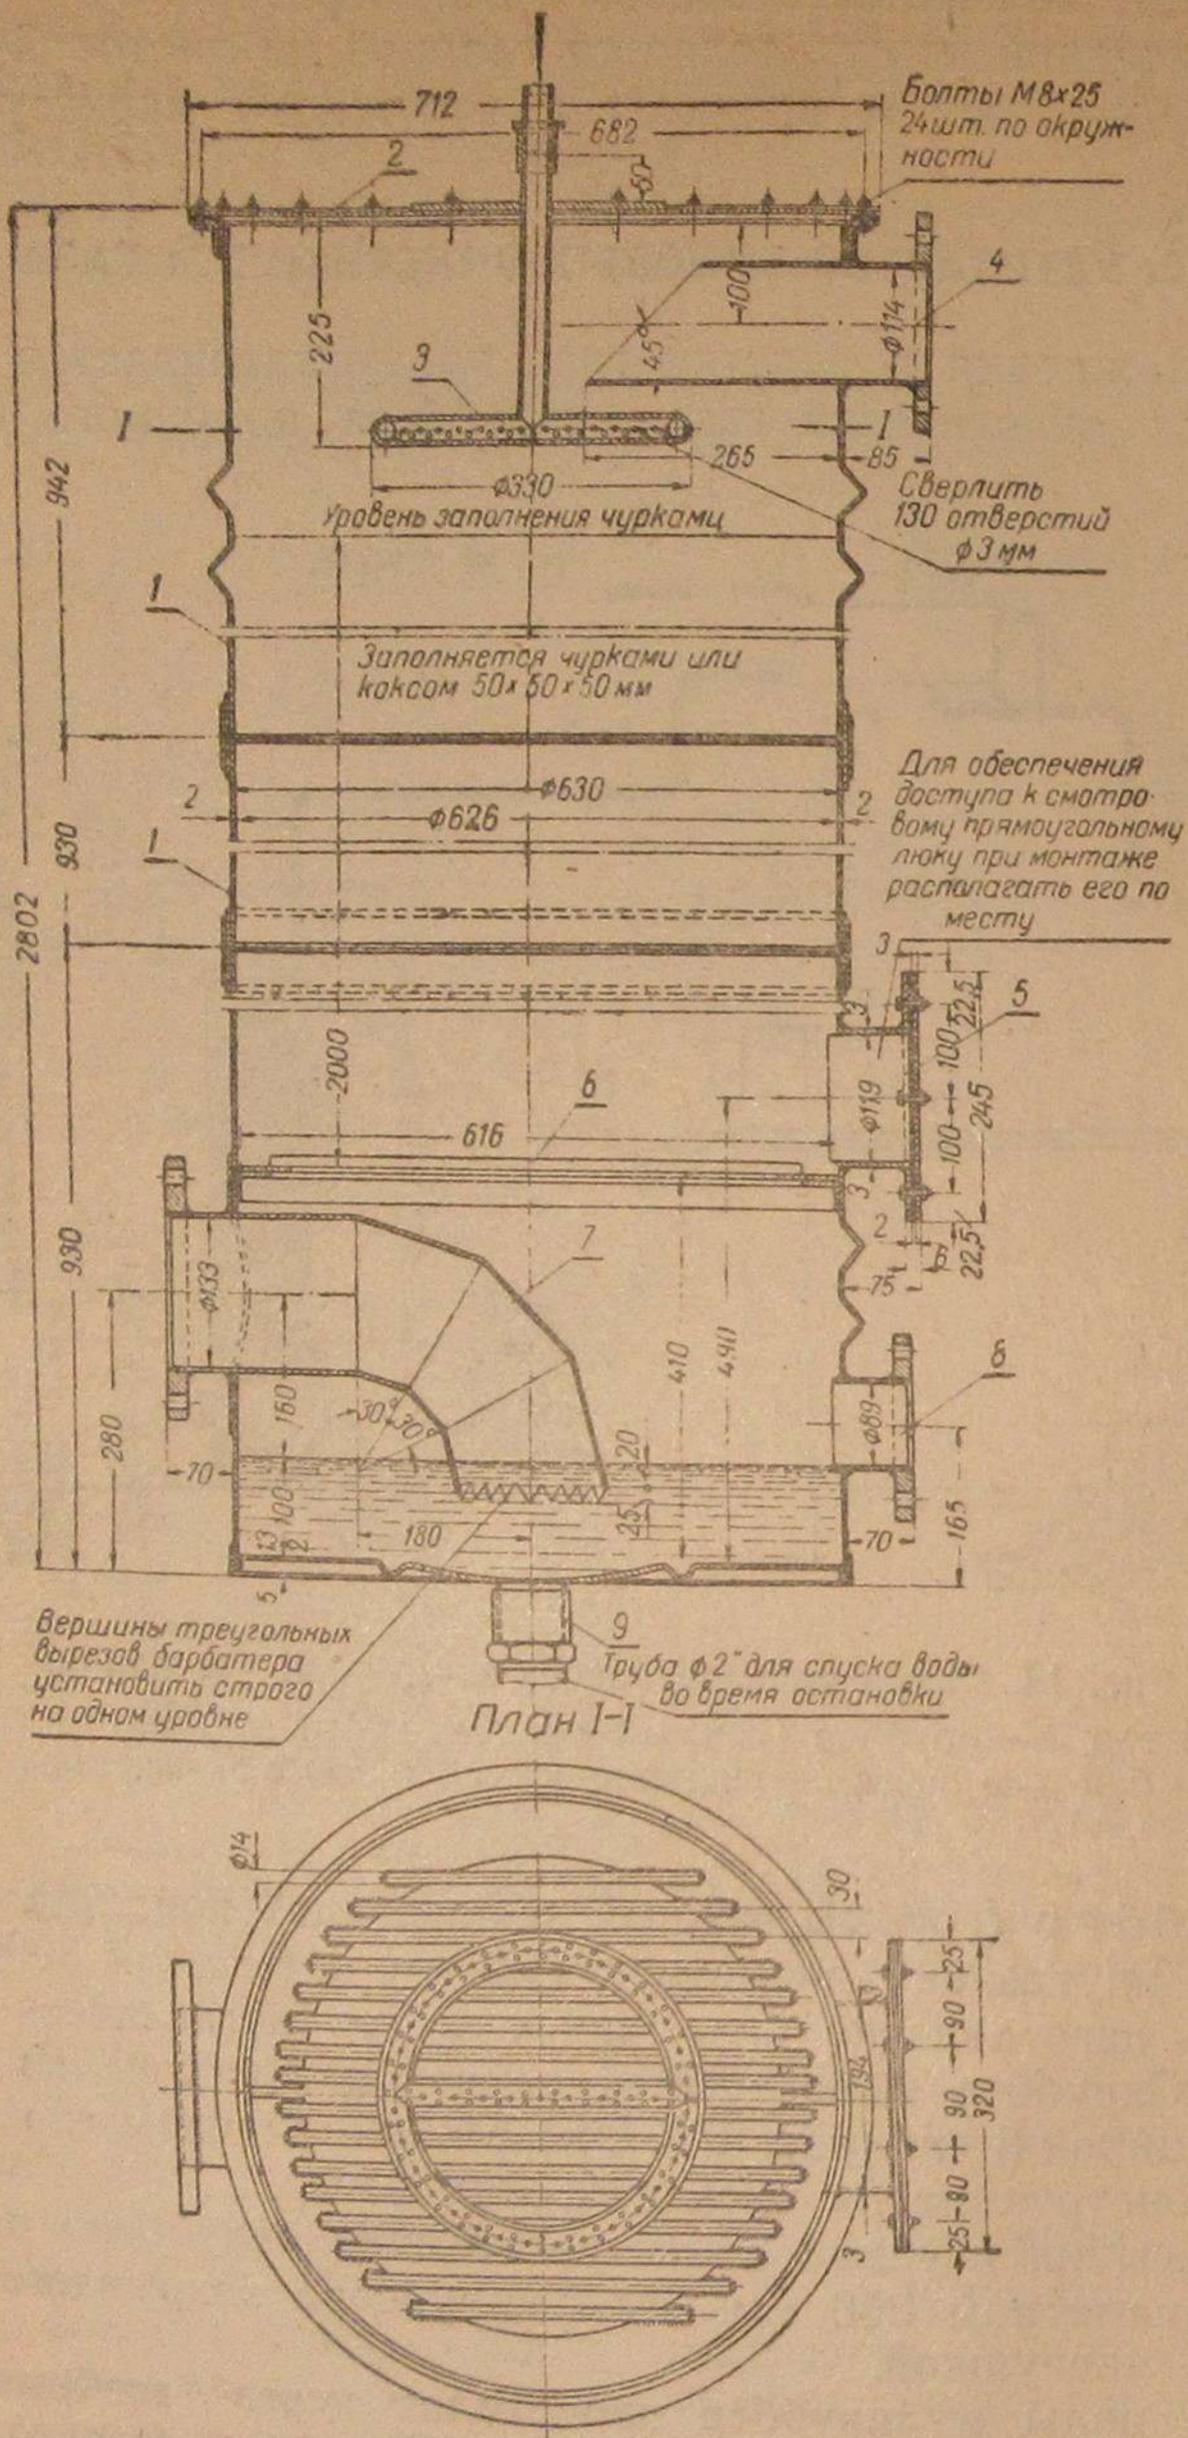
Скру́ббер производительностью 100 м<sup>3</sup> газа в час, изготовленный из старых металлических бочек (I вариант): 1—корпус скру́ббера; 2—крышка скру́ббера; 3—ороситель; 4—газоотводная труба; 5—люк для разгрузки насадок; 6—решётка для укладки насадок; 7—газоподводящая труба (с барбатером); 8—переливная труба; 9—пробка для спуска воды
